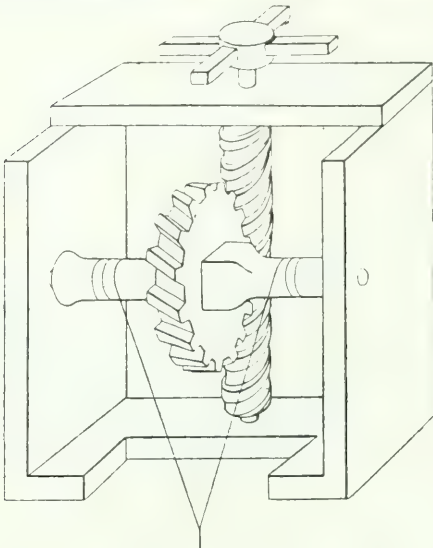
ENGRANAJE DE TORNILLO SIN FIN DE HERÓN
